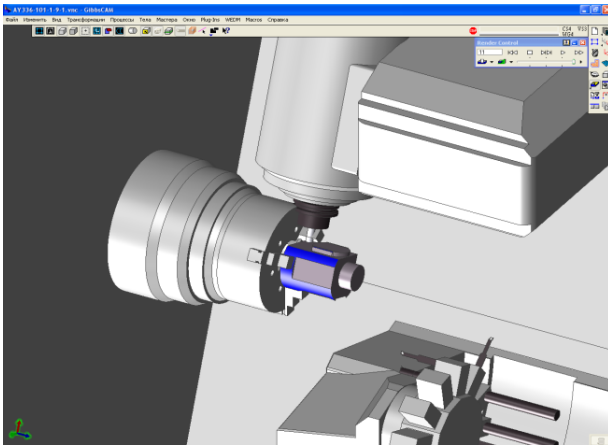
Столкновение фрезерного мотор шпинделя и главного патрона
